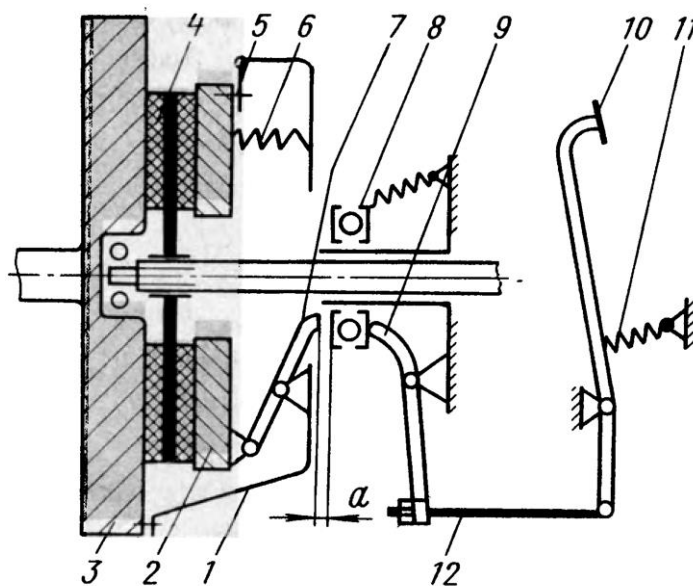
Схема однодискового фрикційного зчеплення
